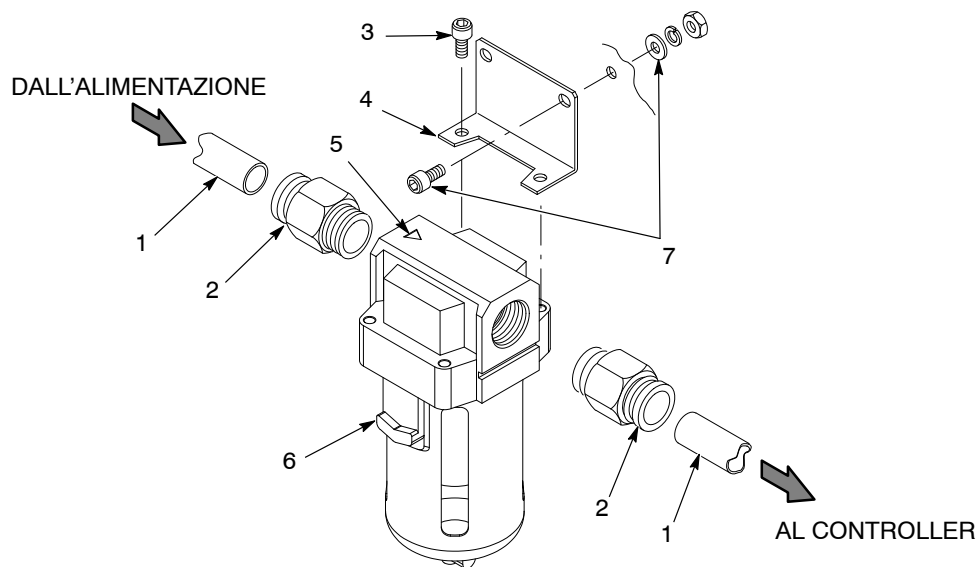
Installazione del filtro dell'aria – Sistemi con montaggio su rotaia e parete
